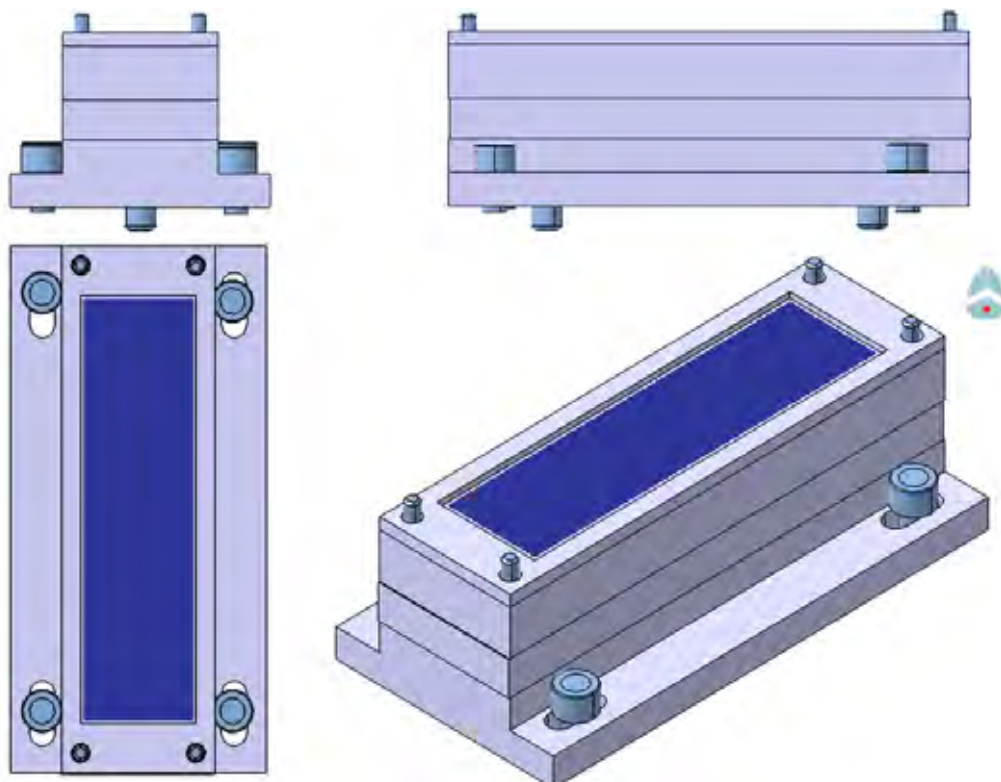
Vistas e perspectiva do banco de ensaios projetado para os ensaios
